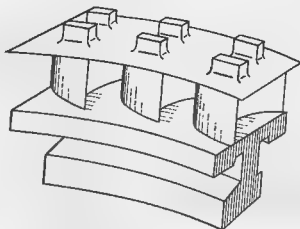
Сварной пакет из трех лопаток для регулирующей ступени
